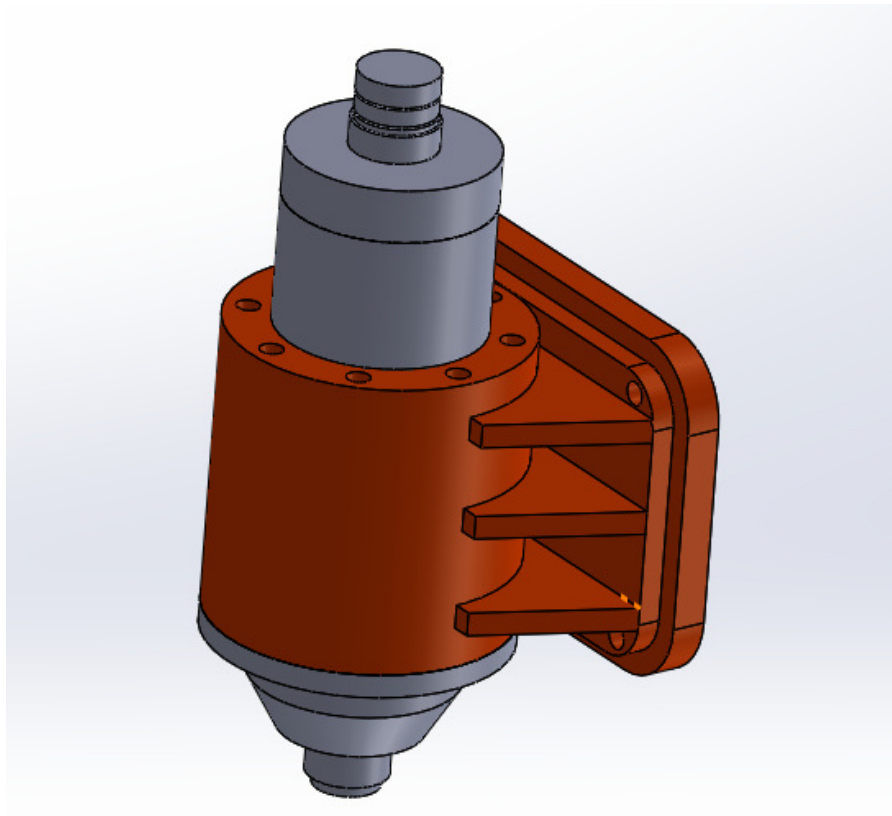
Вид вузла для встановлення мотор шпинделя на консоль верстата
